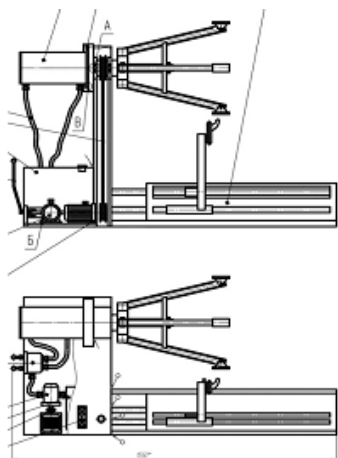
Стенд для монтажа и демонтажа шин колес грузовых автомобилей
